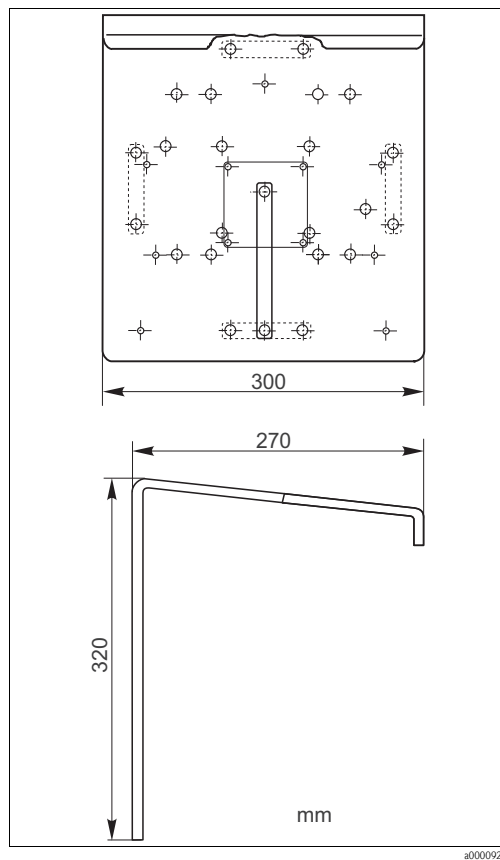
Tettuccio di protezione dalle intemperie CYY101
